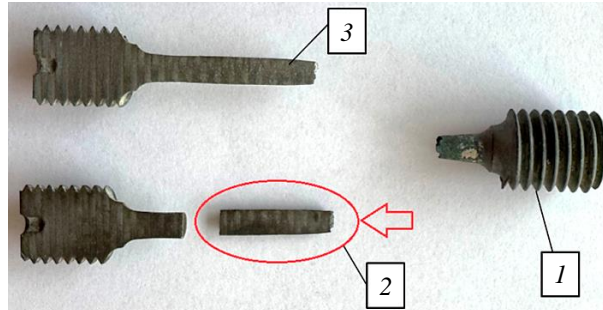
Внешний вид образца из сплава ВЖЛ22, разрушившегося при испытании на длительную прочность: 1 – головка; 2 – исследуемая поверхность; 3 – рабочая часть
